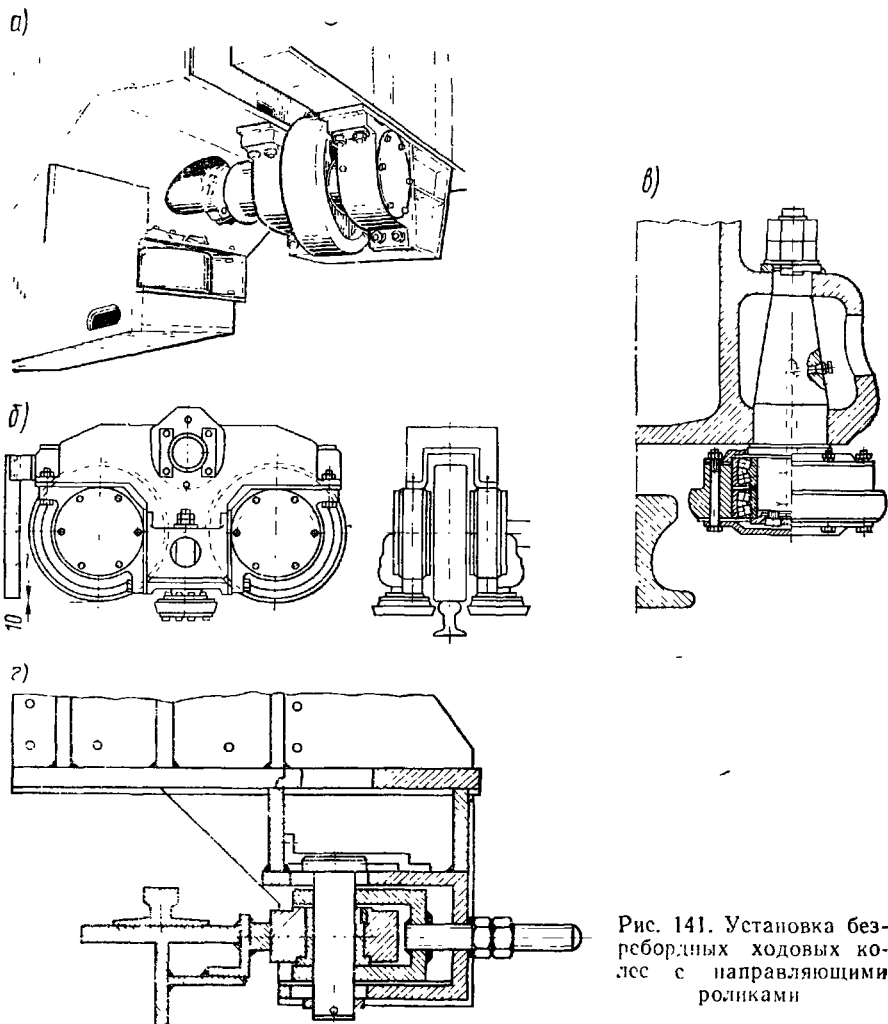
Установка безребордных ходовых колес с направляющими роликами
